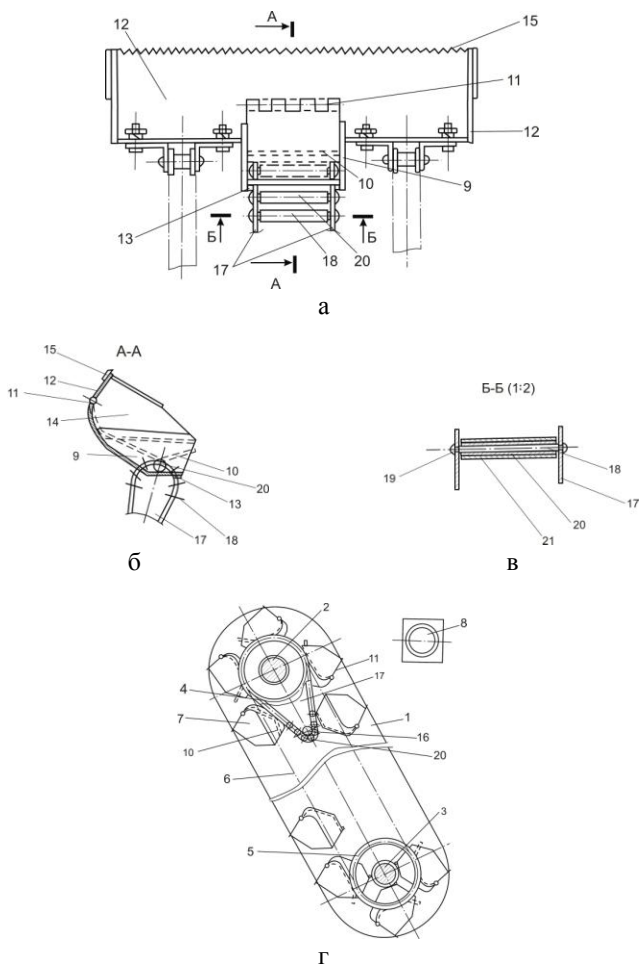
Элеватор с ковшами с подвижными днищами изогнутой формы с дополнительными устройствами в виде роликов: 1 – рама; 2 – приводной вал; 3 – натяжной вал; 4 – приводная звездочка; 5 – натяжная звездочка; 6 – тяговые цепи; 7 – ковши; 8 – привод; 9 – вертикальные ребра; 10 – подвижное днище; 11 – петли шарнирного соединения; 12 – передняя стенка; 13 – упоры; 14 – боковые стенки; 15 – гребенка с зубьями; 16 – дополнительная ось; 17 – пластины; 18 – оси; 19 – отверстия; 20 – ролики; 21 – резина
